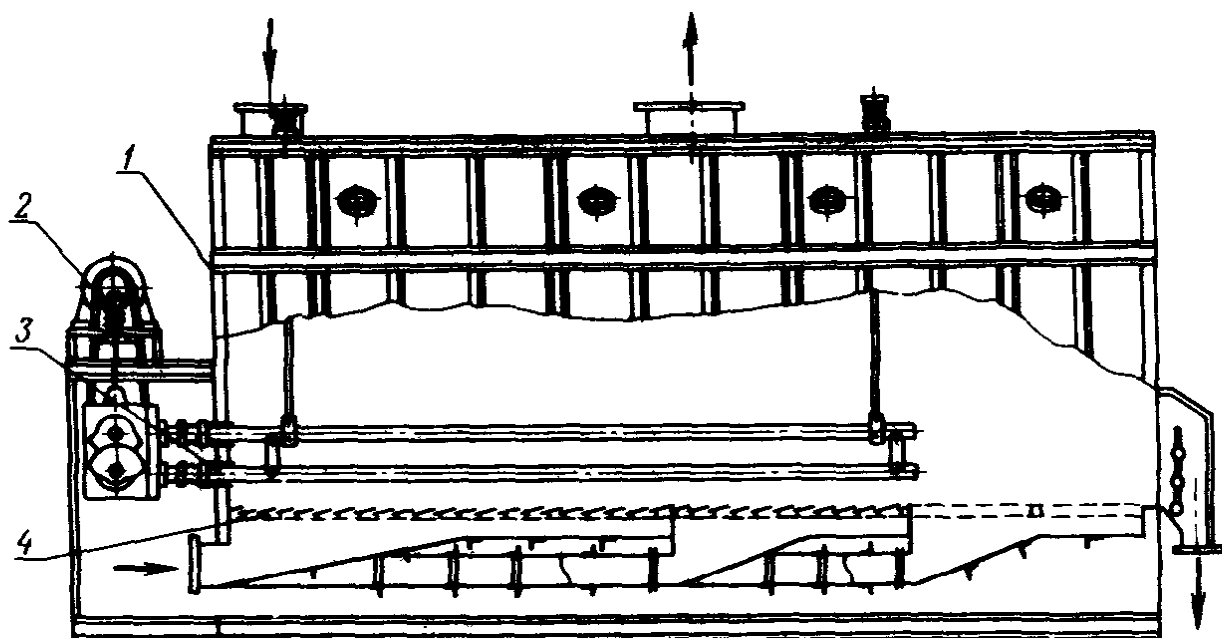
Сушилка кипящего слоя с вибрирующими поверхностями нагрева:
